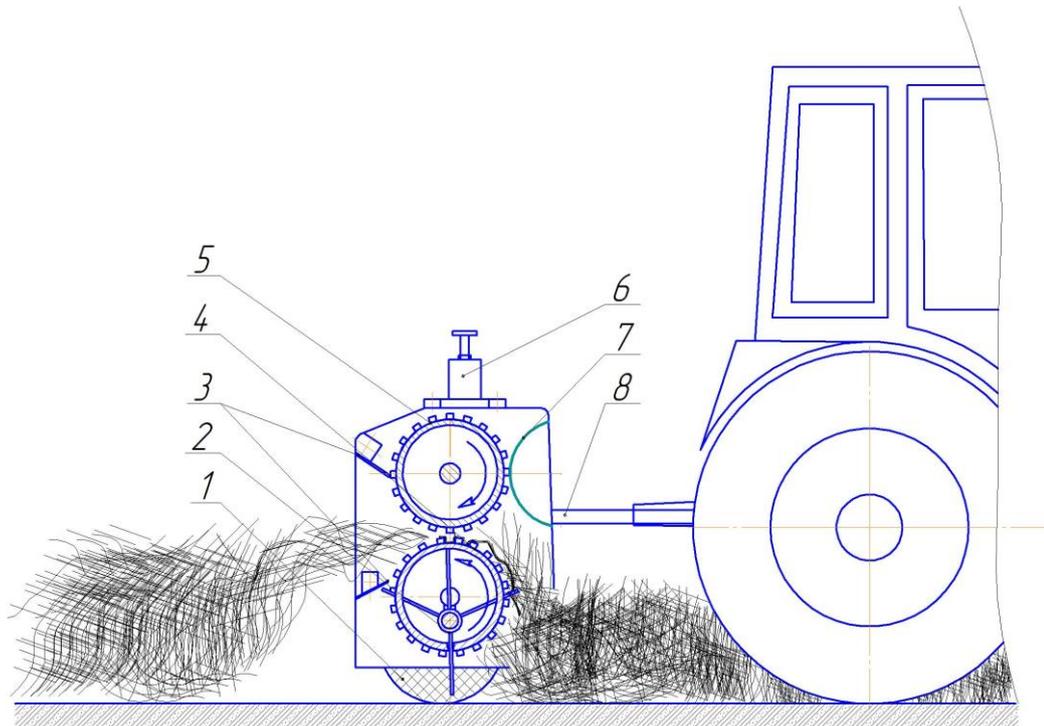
Схема и технологический процесс работы машины для плющения стебельчатых кормов: 1 – опорные пневматические колеса; 2 – подбирающий пальцевый механизм; 3 – чистики; 4, 5 – нижний и верхний плющильные вальцы; 6 – пружинный предохранитель; 7 – отражатель; 8 – прицепное устройство
